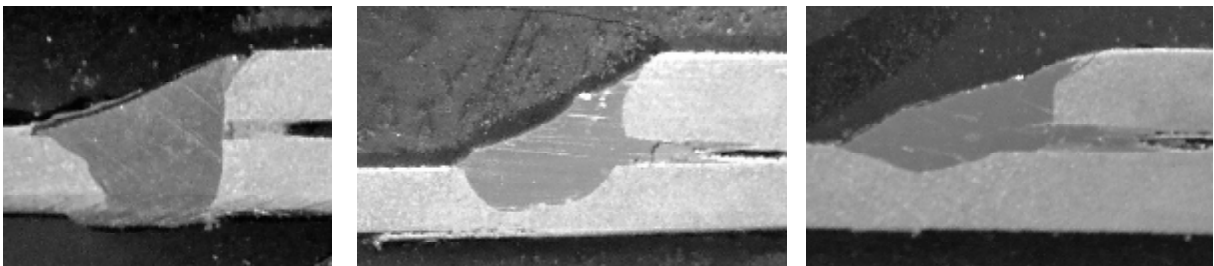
Макрошліфи паяно - зварних з'єднань
